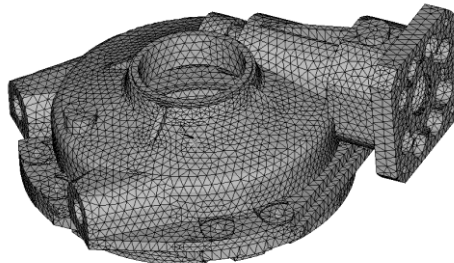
Конечно-элементная модель корпуса спироидного редуктора
